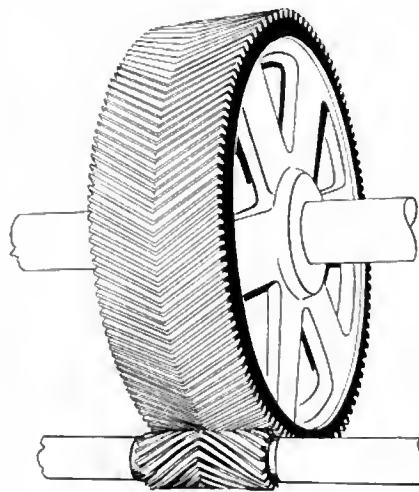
Engrenage à denture à chevrons (Mobil Oil)
